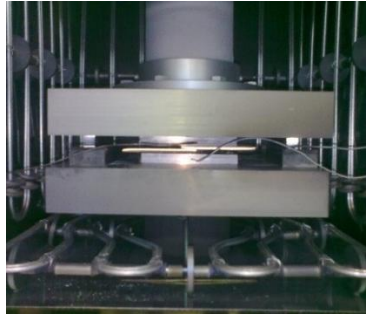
Conjunto composto por prensa, placas de TZM e amostra a ser soldada.
